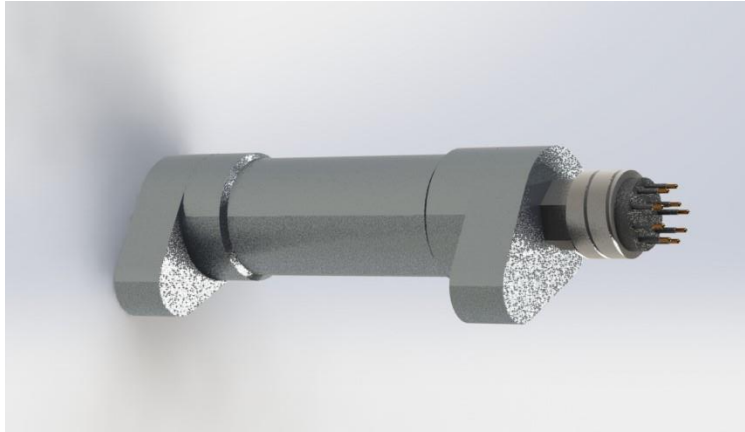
El SVP 70 es la sonda que está montada en el buque Justo Sierra.
